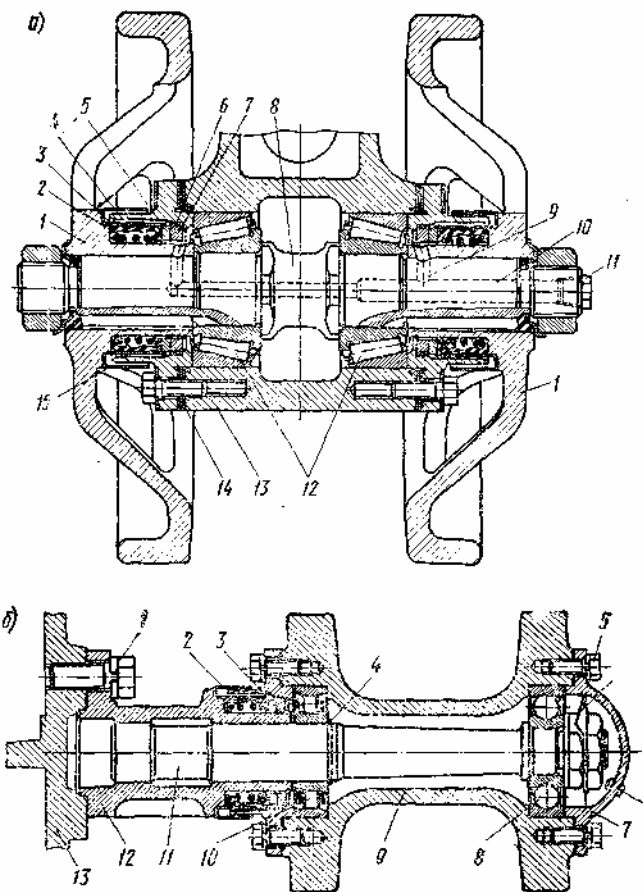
Опорный и поддерживающий катки трактора ДТ-75
